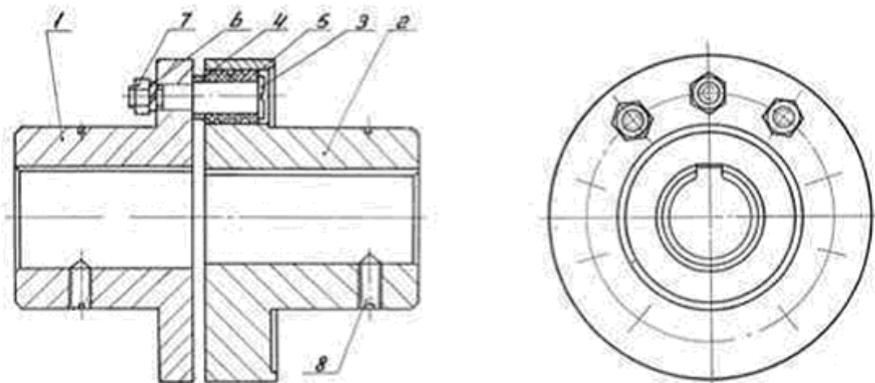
Внешний вид муфты упругой втулочно-пальцевой: 1, 2 – полумуфты; 3 - палец; 4 – втулка распорная; 5 – втулка упругая (допускается выполнять набор колец); 6 – шайба (гровер); 7 – гайка; 8 – установочный винт
